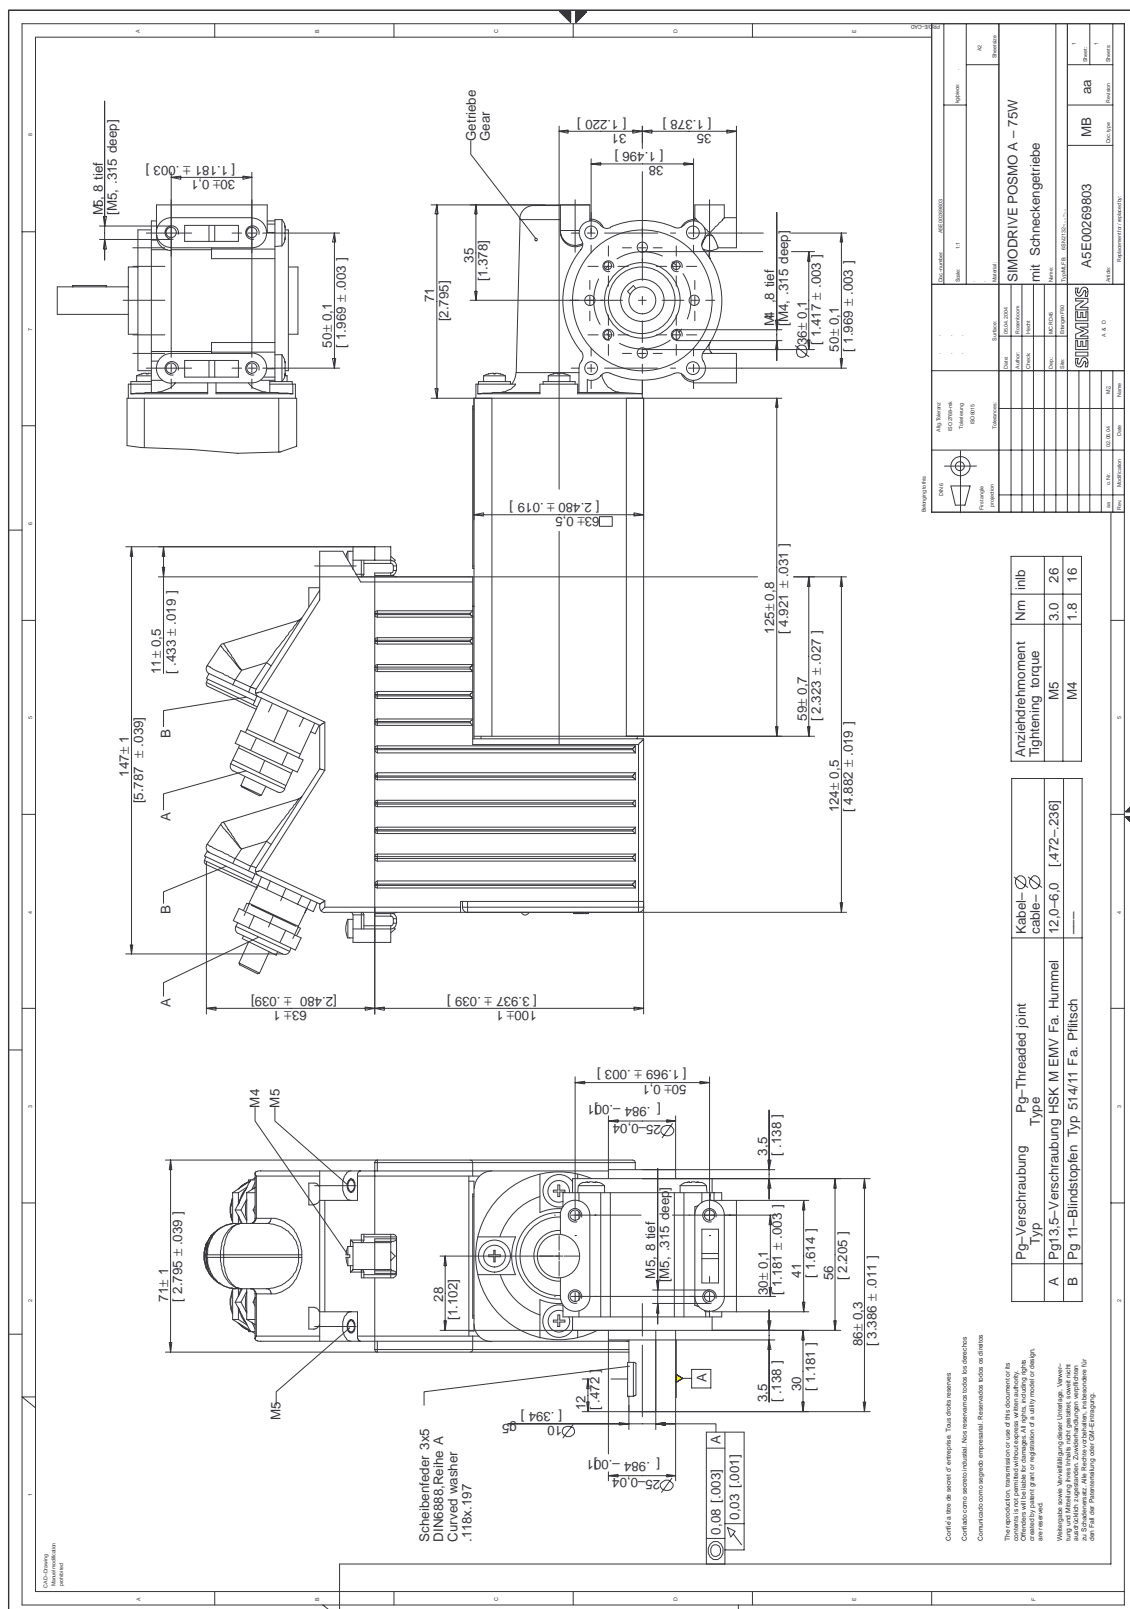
Maßblatt: SIMODRIVE POSMO A – 75 W mit Schneckengetriebe
